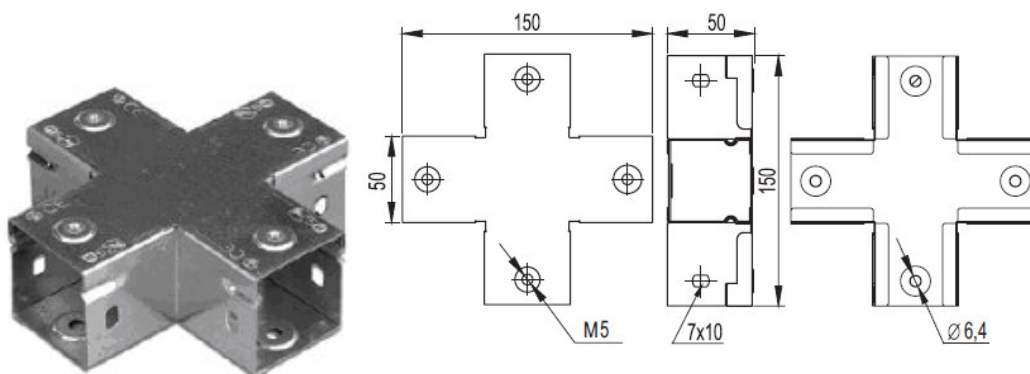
Ответвитель горизонтальный Х-образный глухой, тип 39004
